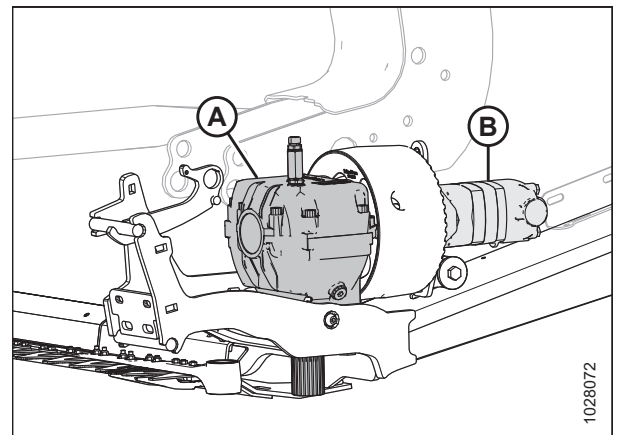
Показано лівий редуктор привода ножа — правий аналогічний лівому
